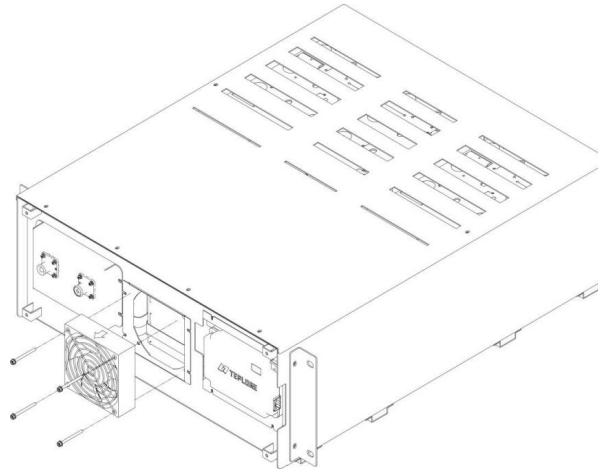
Reemplazo del ventilador del paquete de baterías
